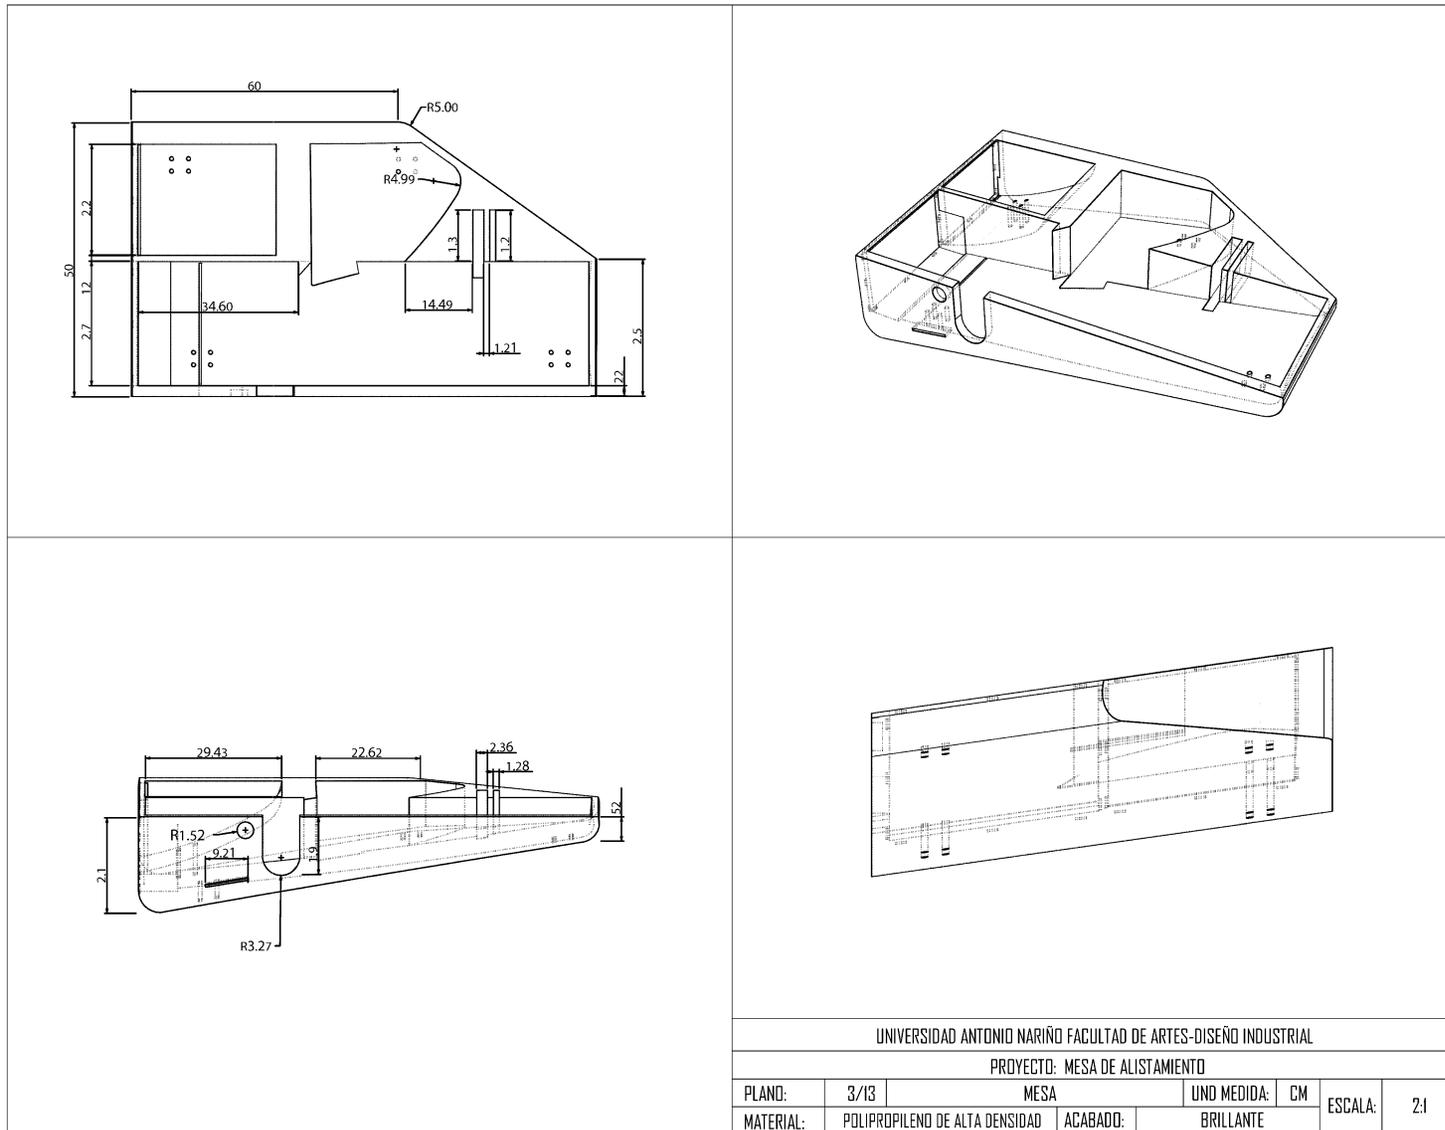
Planos piezas 2 (Elaboración propia, 2020)
